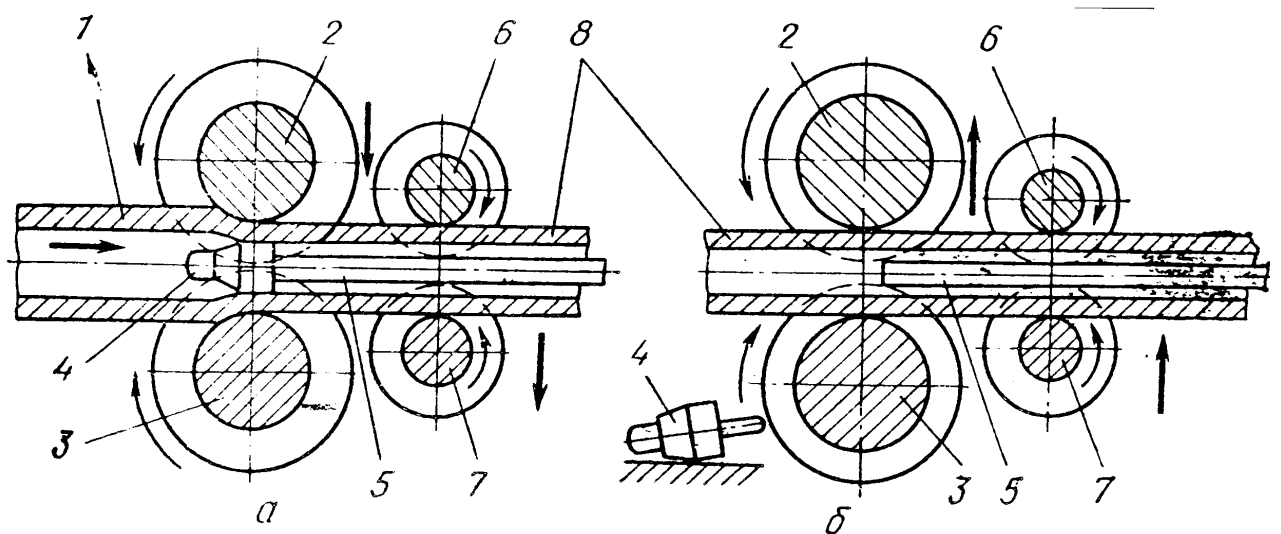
Схема прокатки труб на автоматстане: *а* – прокатка; *б* – возврат трубы; 1 – гильза; 2 – верхний валок; 3 – нижний валок; 4 – оправка; 5 – упорный стержень; 6 – верхний ролик обратной подачи; 7 – нижний ролик обратной подачи; 8 – труба
